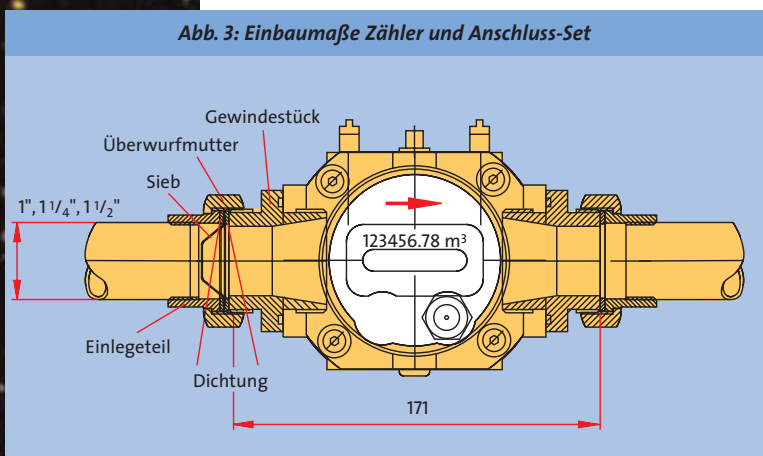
Einbaumaße Zähler und Anschluss-Set
